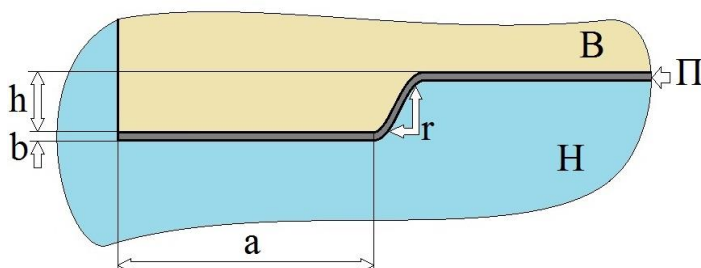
Геометрия приспособления для выравнивания входных каналов: Н – нижняя формообразующая; В – верхняя формообразующая; П – пластина; h – глубина вытяжки; b – толщина листа; a – ширина сварочной полки; r – радиусы гибки
